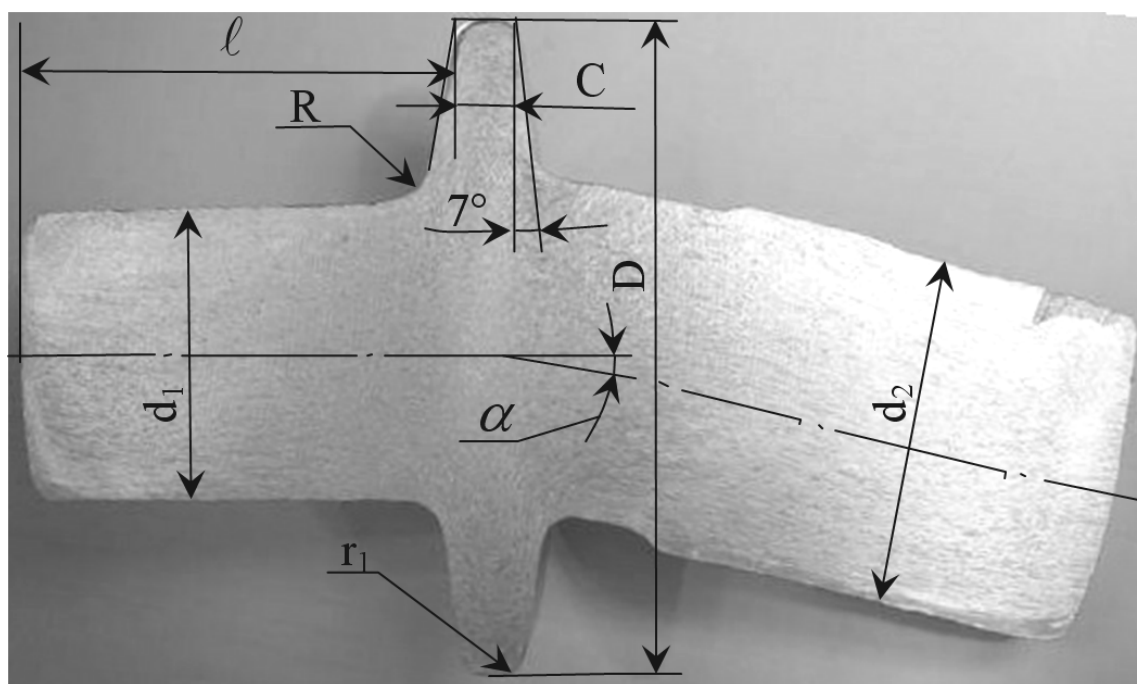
Третья группа типовых представителей вальцуемых заготовок на ковочных вальцах. Макроструктура продольного сечения штампованной поковки, изготовленной из вальцованной заготовки с ее поворотом на 180° , для получения второго конца
